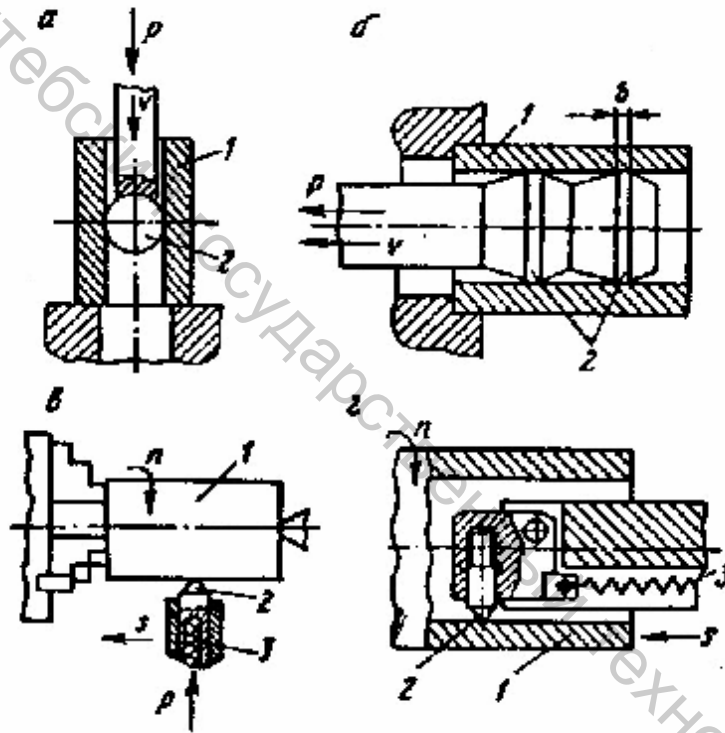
Схемы обработки способами ППД со скольжением инструментов: 1- заготовка; 2- инструмент; 3- пружина
